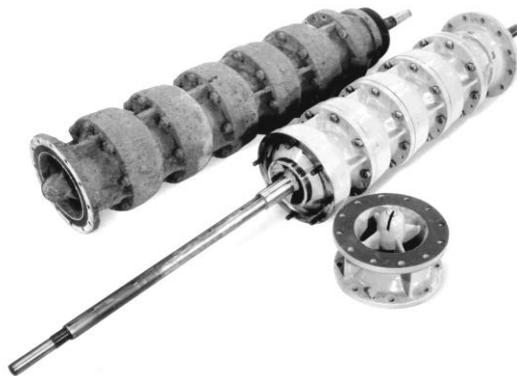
Der hydraulische Teil einer Bohrlochwellenpumpe, vor und nach der Revision
